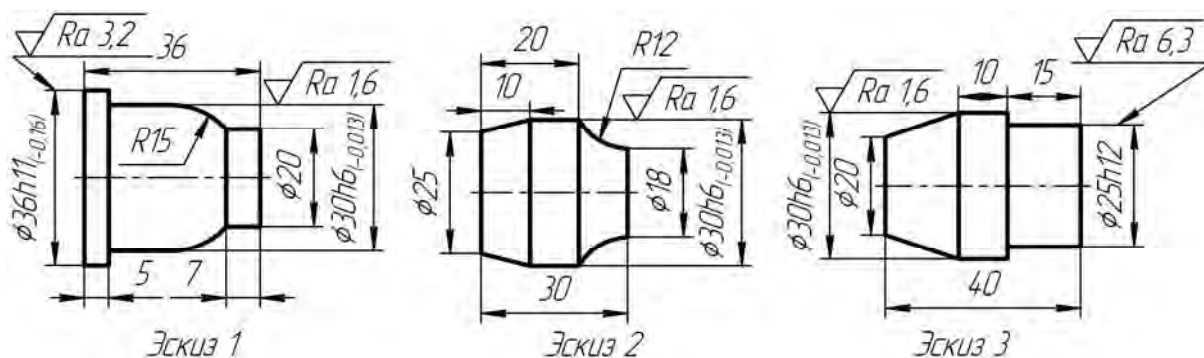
Эскизы деталей для расчета фасонных резцов
